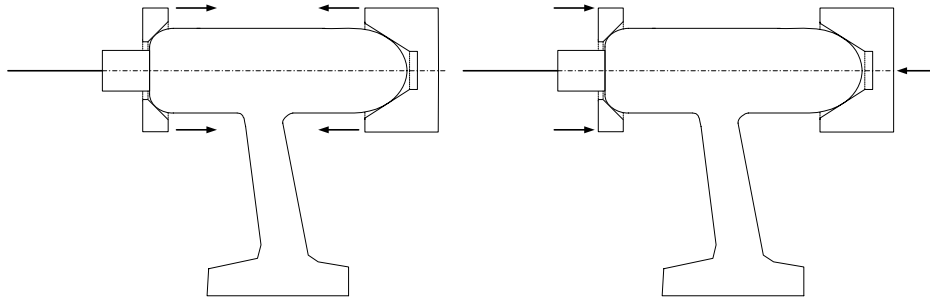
Bohrschrauber zwischen zwei Formelementen
